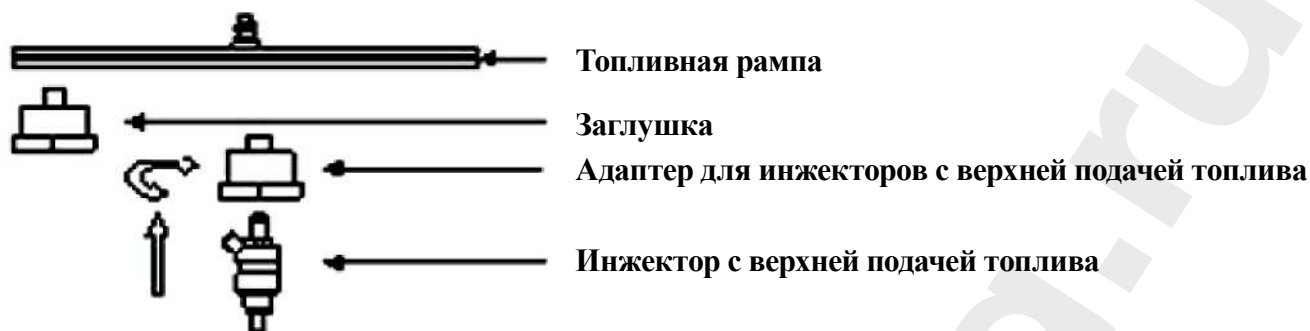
Установка адаптера инжектора с верхней подачей топлива
